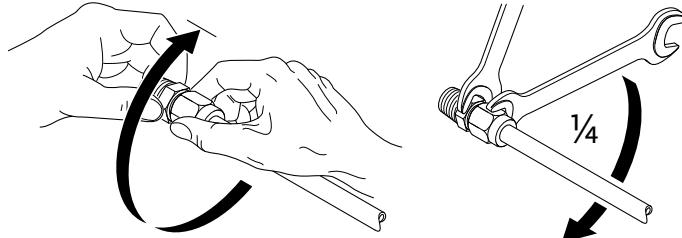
Допълнително завъртане на компресионния фитинг с  $1/4$  оборот
